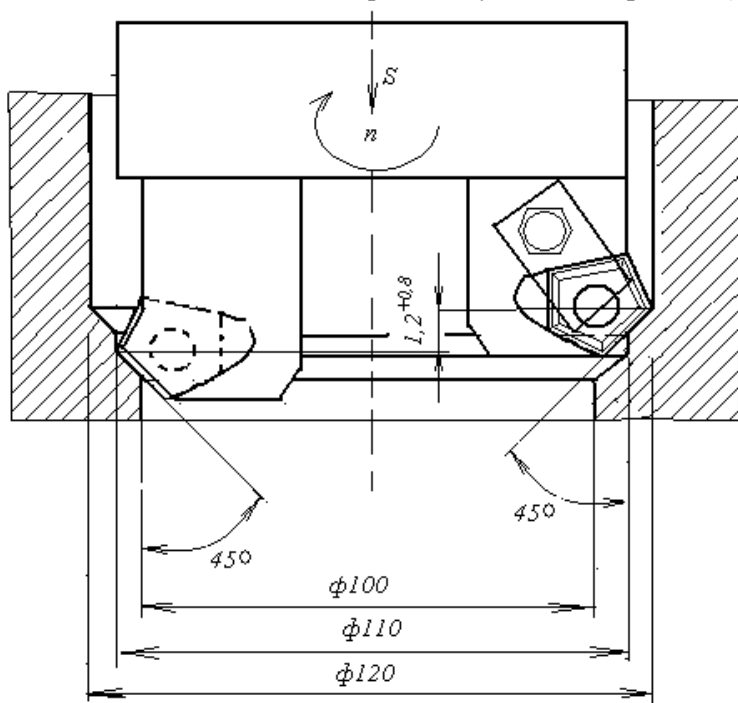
Растачивание отверстия на одной из позиций шестишпindelного токарного вертикального полуавтомата двумя резцами Т5К10, $\varphi = 45^\circ$
